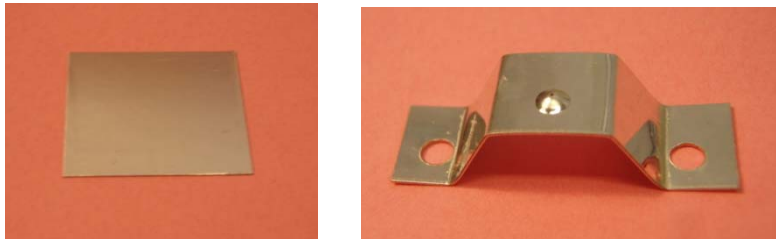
Contact sphère plan modèle. a) plan, b) pion
